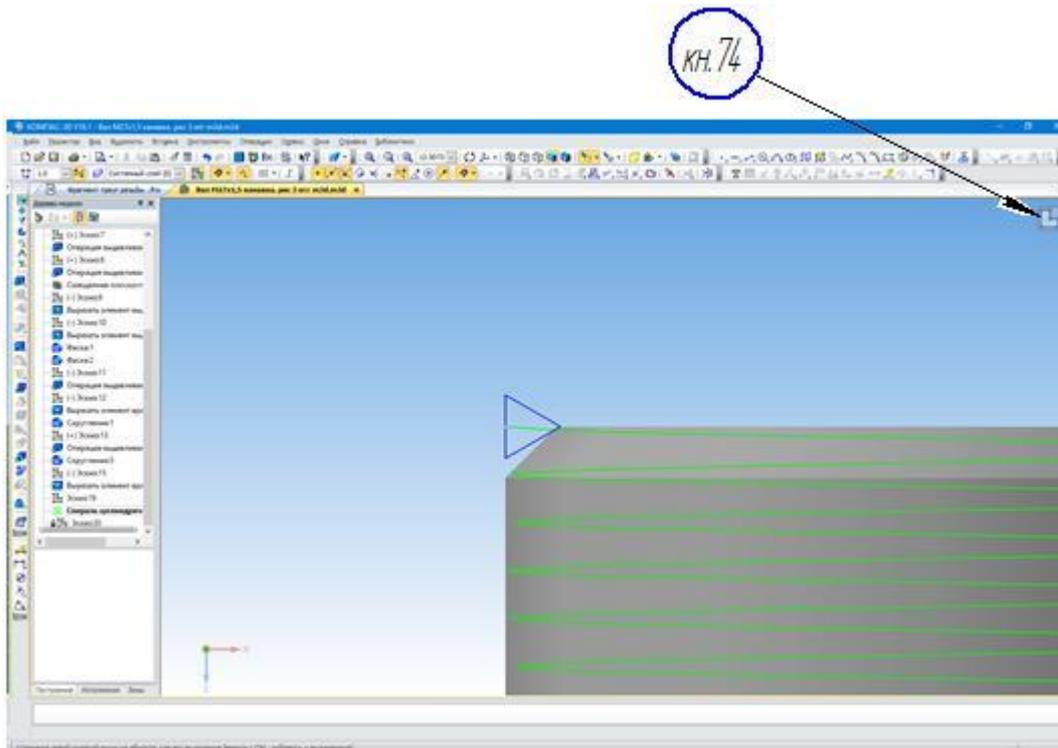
Установка эскиза профиля резьбовой поверхности
